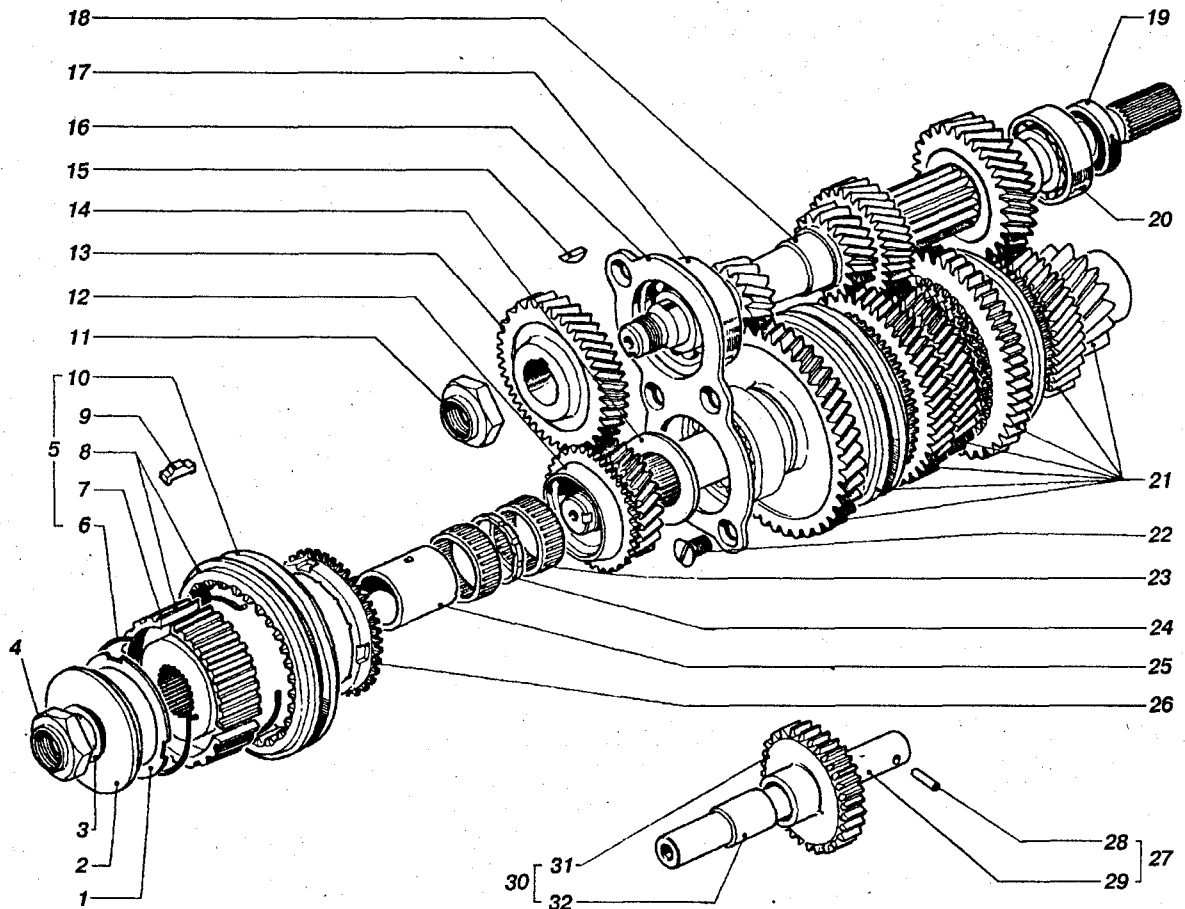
Детали коробки передач (пятая и главная передачи): 1 – шайба дистанционная; 2 – шайба упорная сухарей синхронизатора пятой передачи; 3 – кольцо; 4 – гайка; 5 – муфта включения синхронизатора пятой передачи в сборе; 6 – пружина синхронизатора третьей и четвертой передач; 7 – ступица синхронизатора пятой передачи; 8 – муфта со ступицей в сборе; 9 – сухарь синхронизатора; 10 – муфта включения синхронизатора пятой передачи; 11 – гайка; 12 – шестерня ведомая пятой передачи; 13 – шестерня ведущая пятой передачи; 14 – шайба упорная; 15 – шпонка; 16 – крышка подшипников; 17 – подшипник задний (6-126805E); 18 – вал ведущий в сборе; 19 – манжета; 20 – подшипник передний (66-42205AE); 21 – шестерня ведущая главной передачи в сборе; 22 – винт; 23 – подшипник ведомых шестерён второй и третьей передач (464606E или 3K32x37x13E); 24 – проставочное кольцо; 25 – распорная втулка; 26 – кольцо синхронизатора третьей и четвертой передач; 27 – ось в сборе; 28 – штифт; 29 – ось; 30 – шестерня паразитная заднего хода в сборе; 31 – шестерня паразитная заднего хода; 32 – ось в сборе
